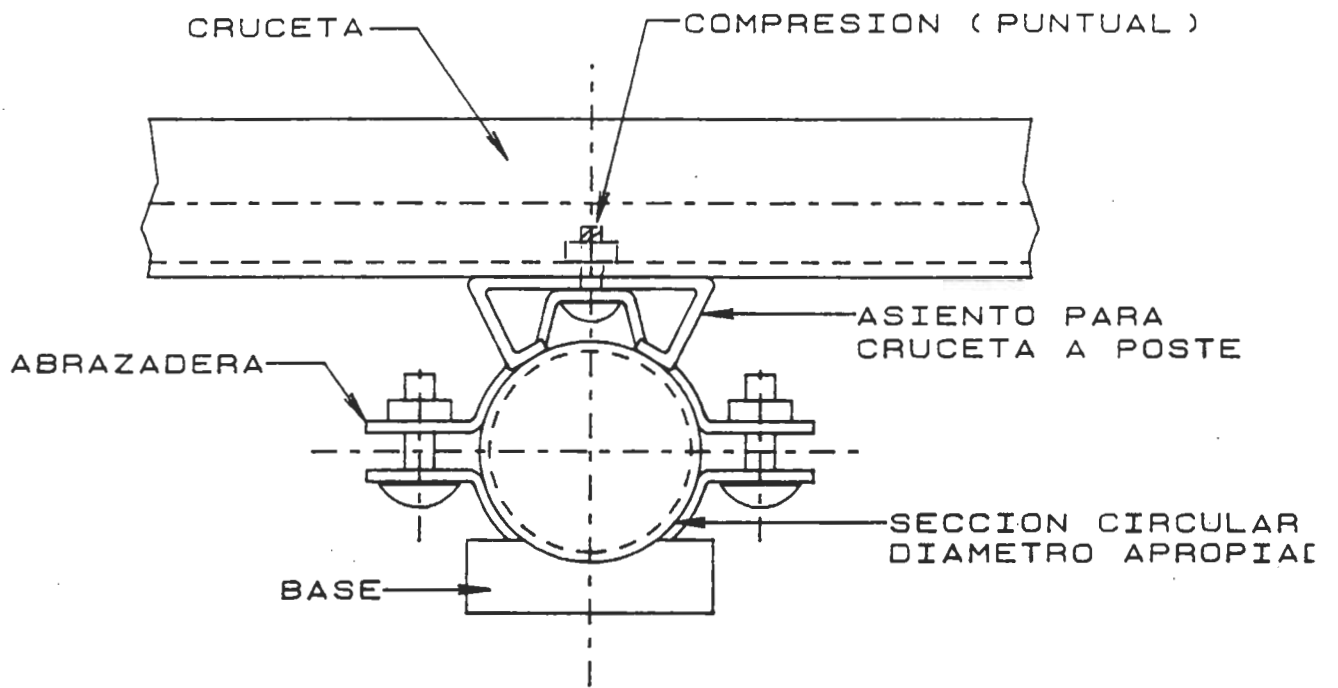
MONTAJE DEL ENSAYO DE COMPRESION
